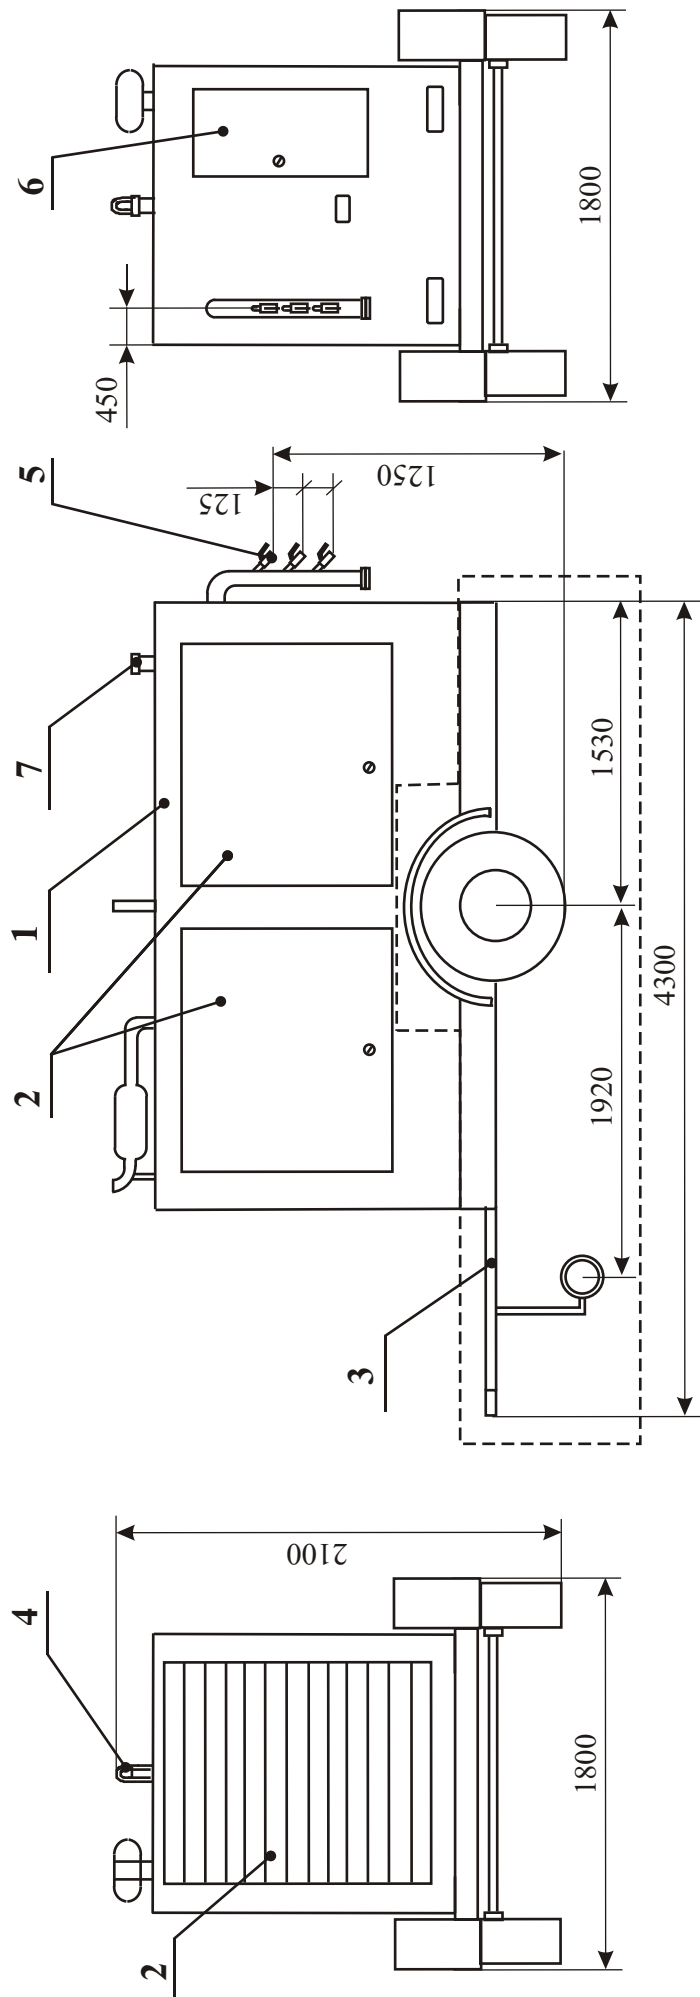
Габаритные и присоединительные размеры компрессорной станции
